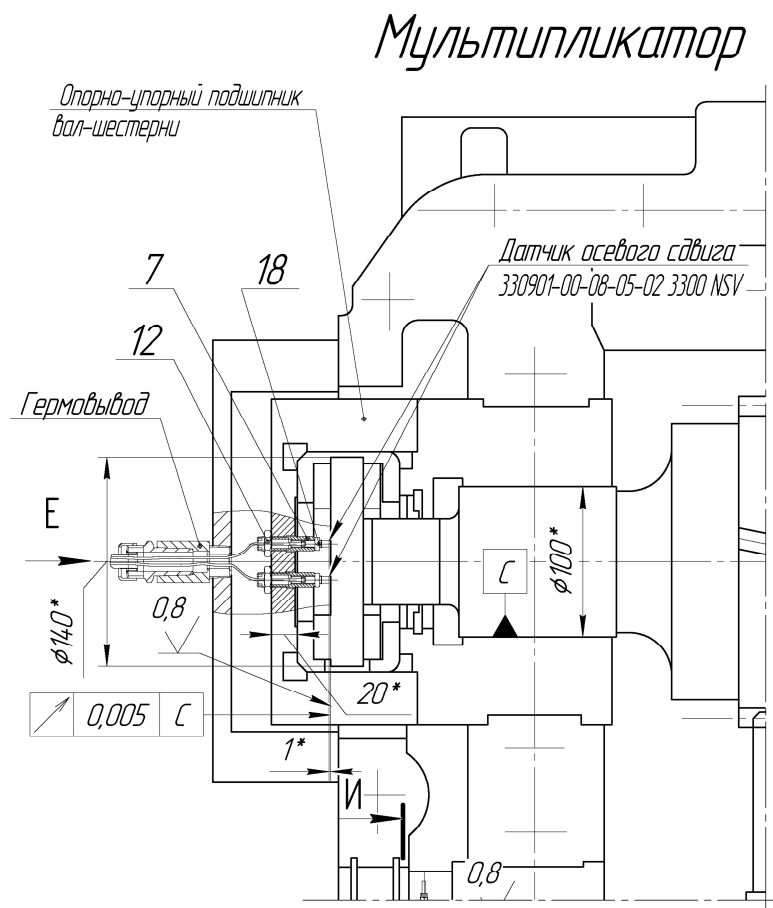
Схема установки датчиков осевого сдвига вал-шестерни мультипликатора компрессора поз.101J
